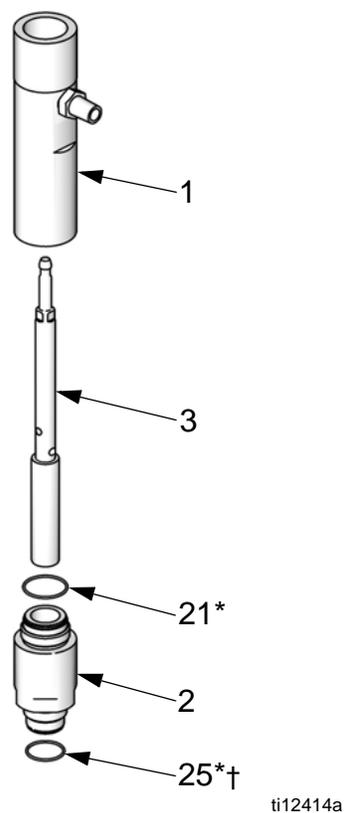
Assemblage de l'ensemble de piston/tige et les cylindres.
